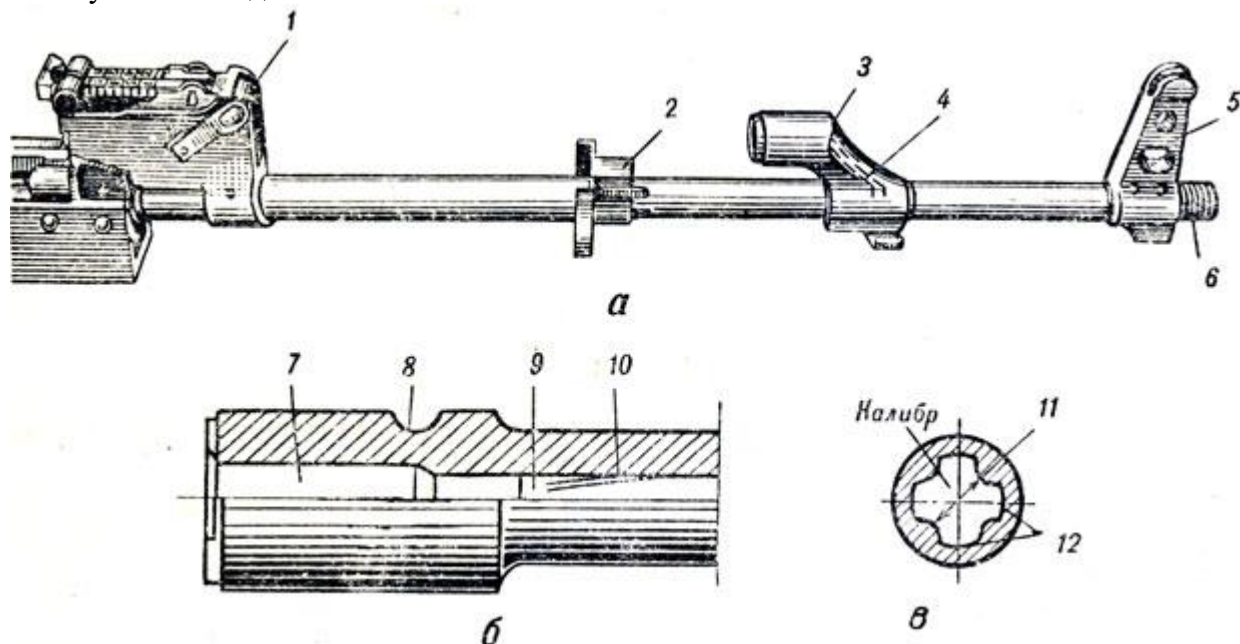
Ствол: а - общий вид; б - казенная часть в разрезе; в - сечение ствола; 1 - колодка прицела; 2 - соединительная муфта; 3 - газовая камера; 4 - газоотводное отверстие; 5 - основание мушки; 6 - резьба; 7 - патронник; 8 - выем для шпильки ствола; 9 - пультный вход; 10 - нарезная часть; 11 - поле; 12 - нарезы
